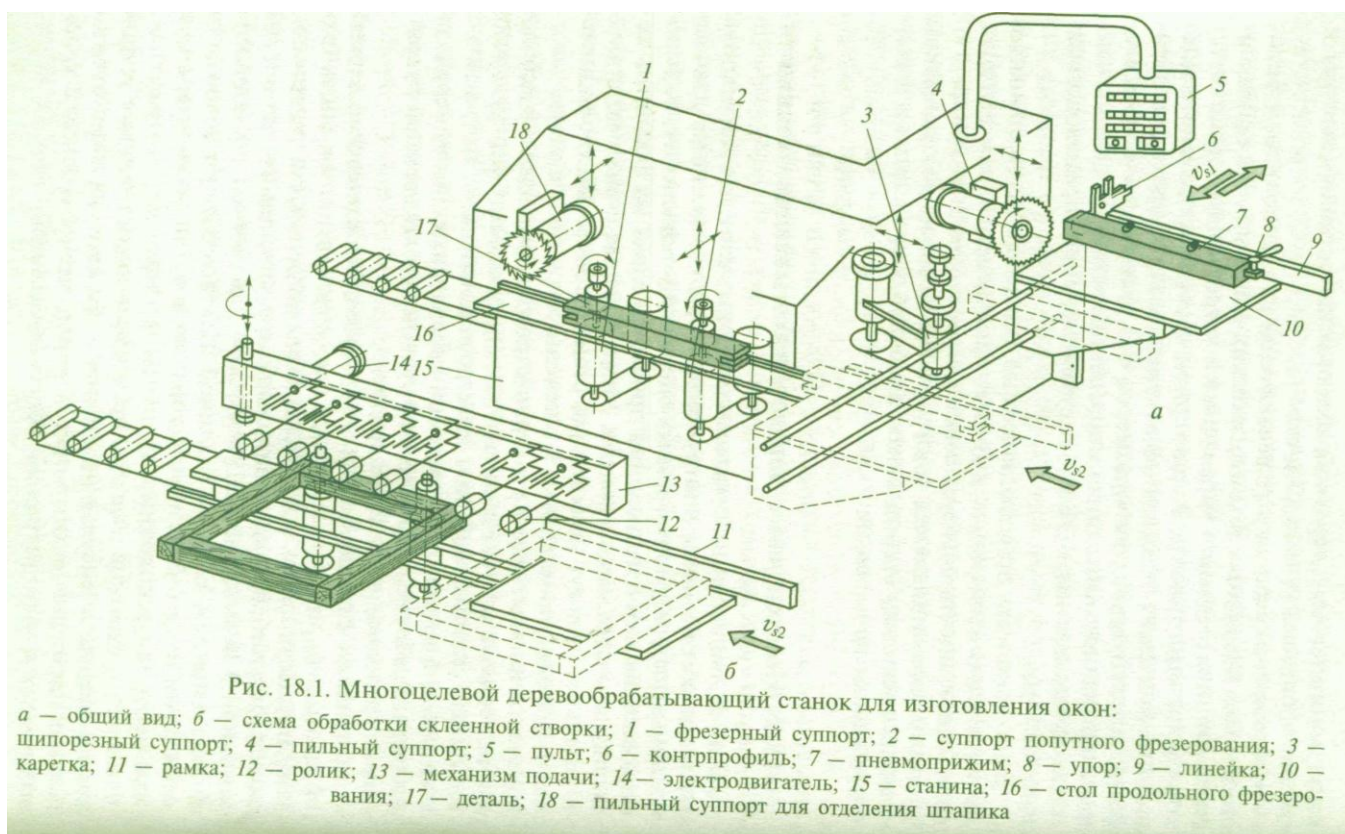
Многоцелевой деревообрабатывающий станок для изготовления окон:
